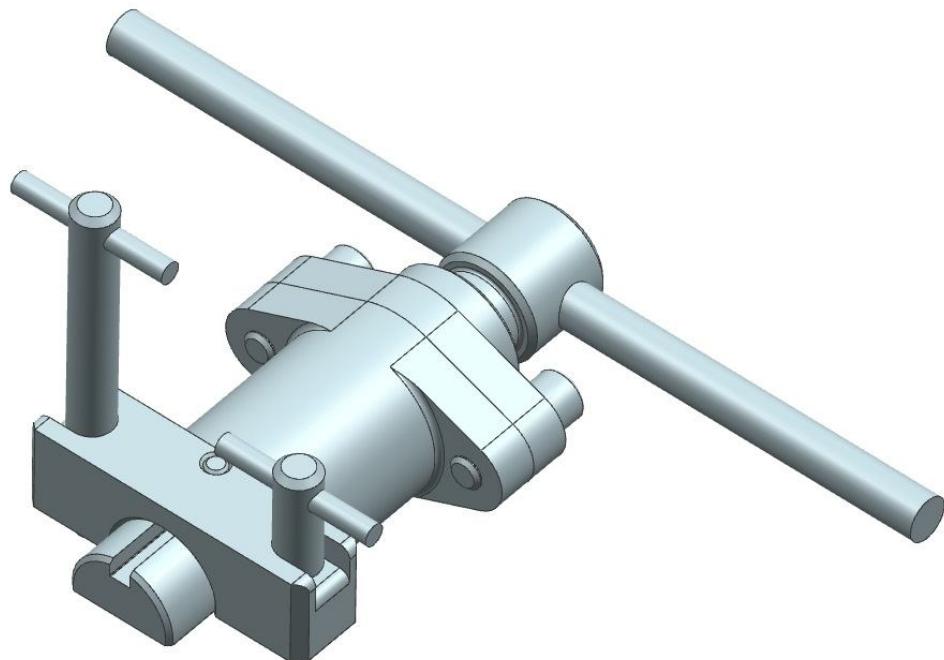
ЗМ 7823-4815, Приспособление для снятия масляного картера
